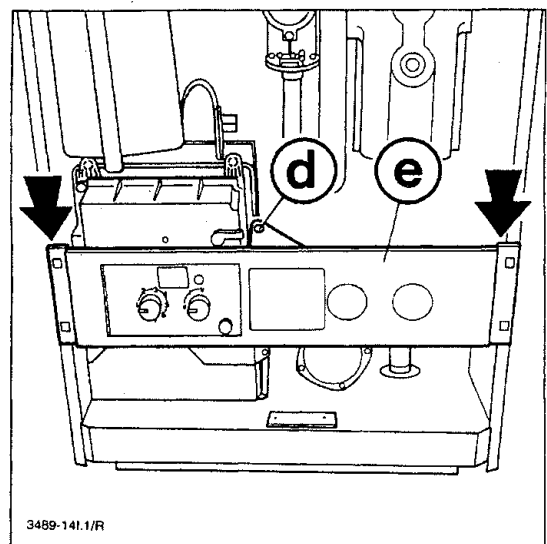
Rimontare la plancia (e) e assicurarla con la vite (d)
